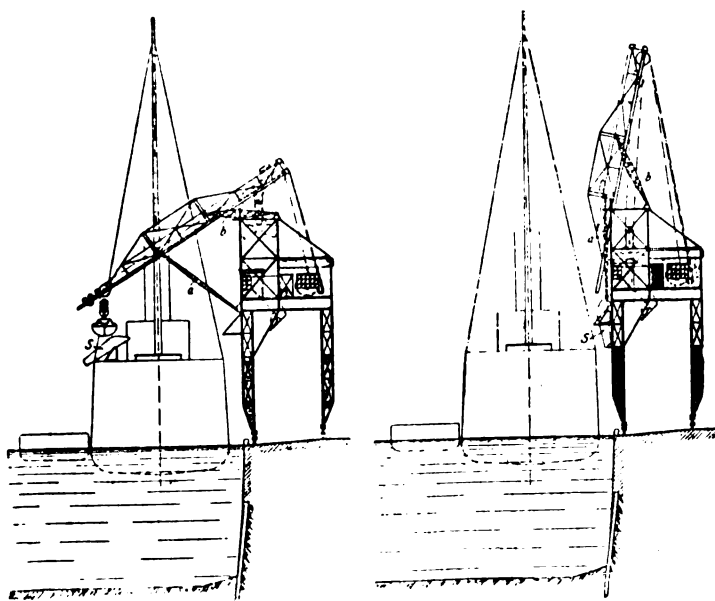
e 47. — Scaricatore a braccio articolato ad Amburgo.
